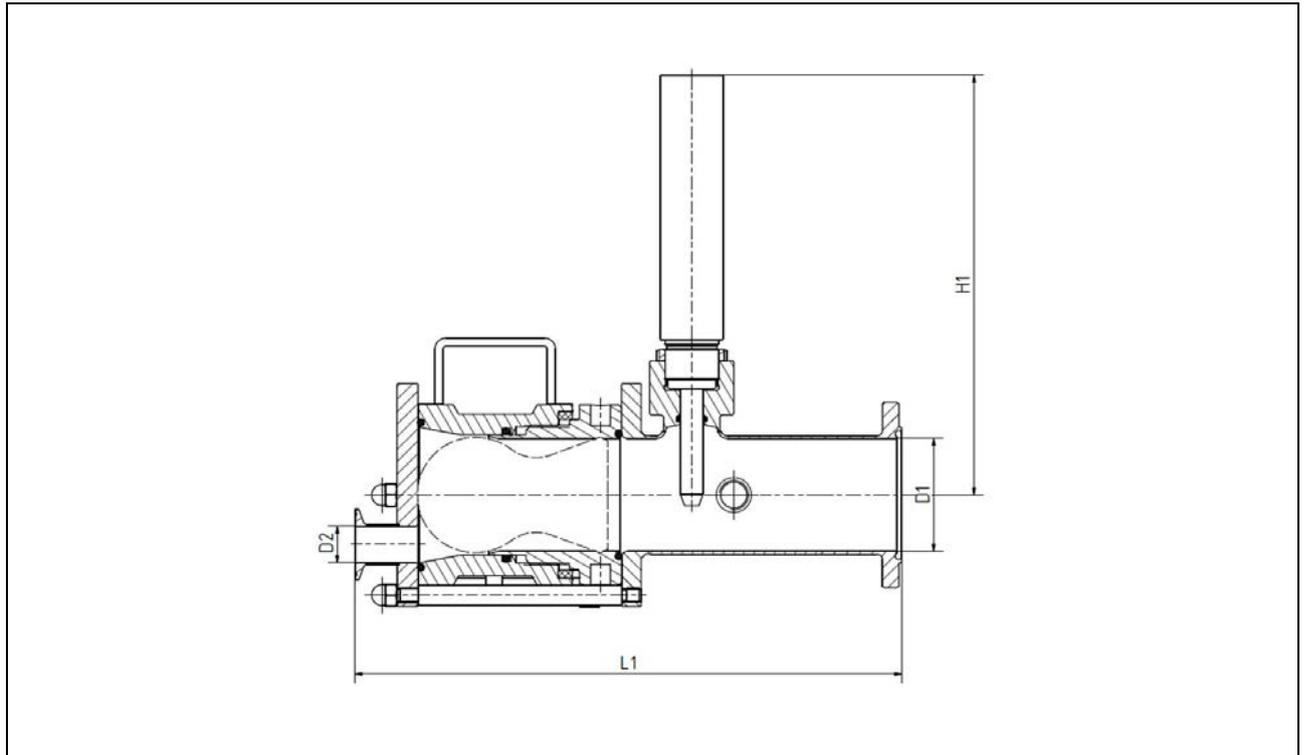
Steckkammer mit Stopper, Anschlussvariante ISO, Serie C
